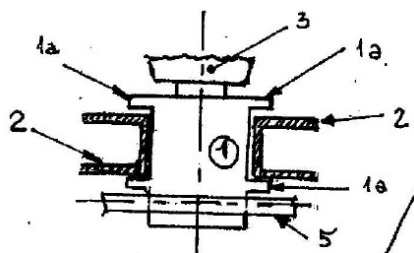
Guida prismatica tradizionale vista dall'alto
